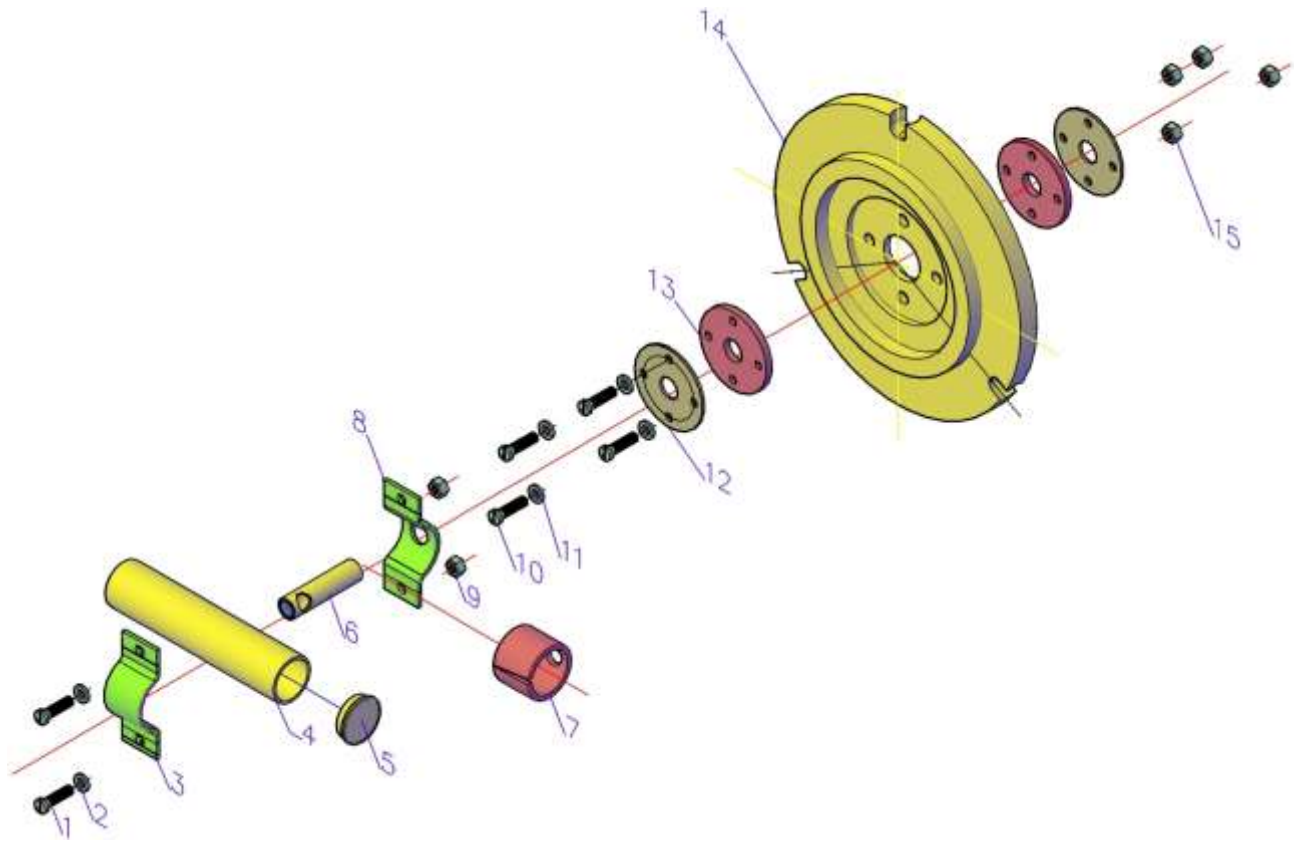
Деталювальна схема вузла кріплення фрагмента РТ з досліджуваною насадкою: 1,10 – болти; 2, 11, 12 – шайби; 3, 8 – монтажні хомути; 4 – фрагмент РТ; 5 – заглушка на торці РТ; 6 – вихідна насадка; 7, 13 - гумові прокладки; 9, 15 – гайки; 14- торцева кришка передньої основи напірного бака [80]
